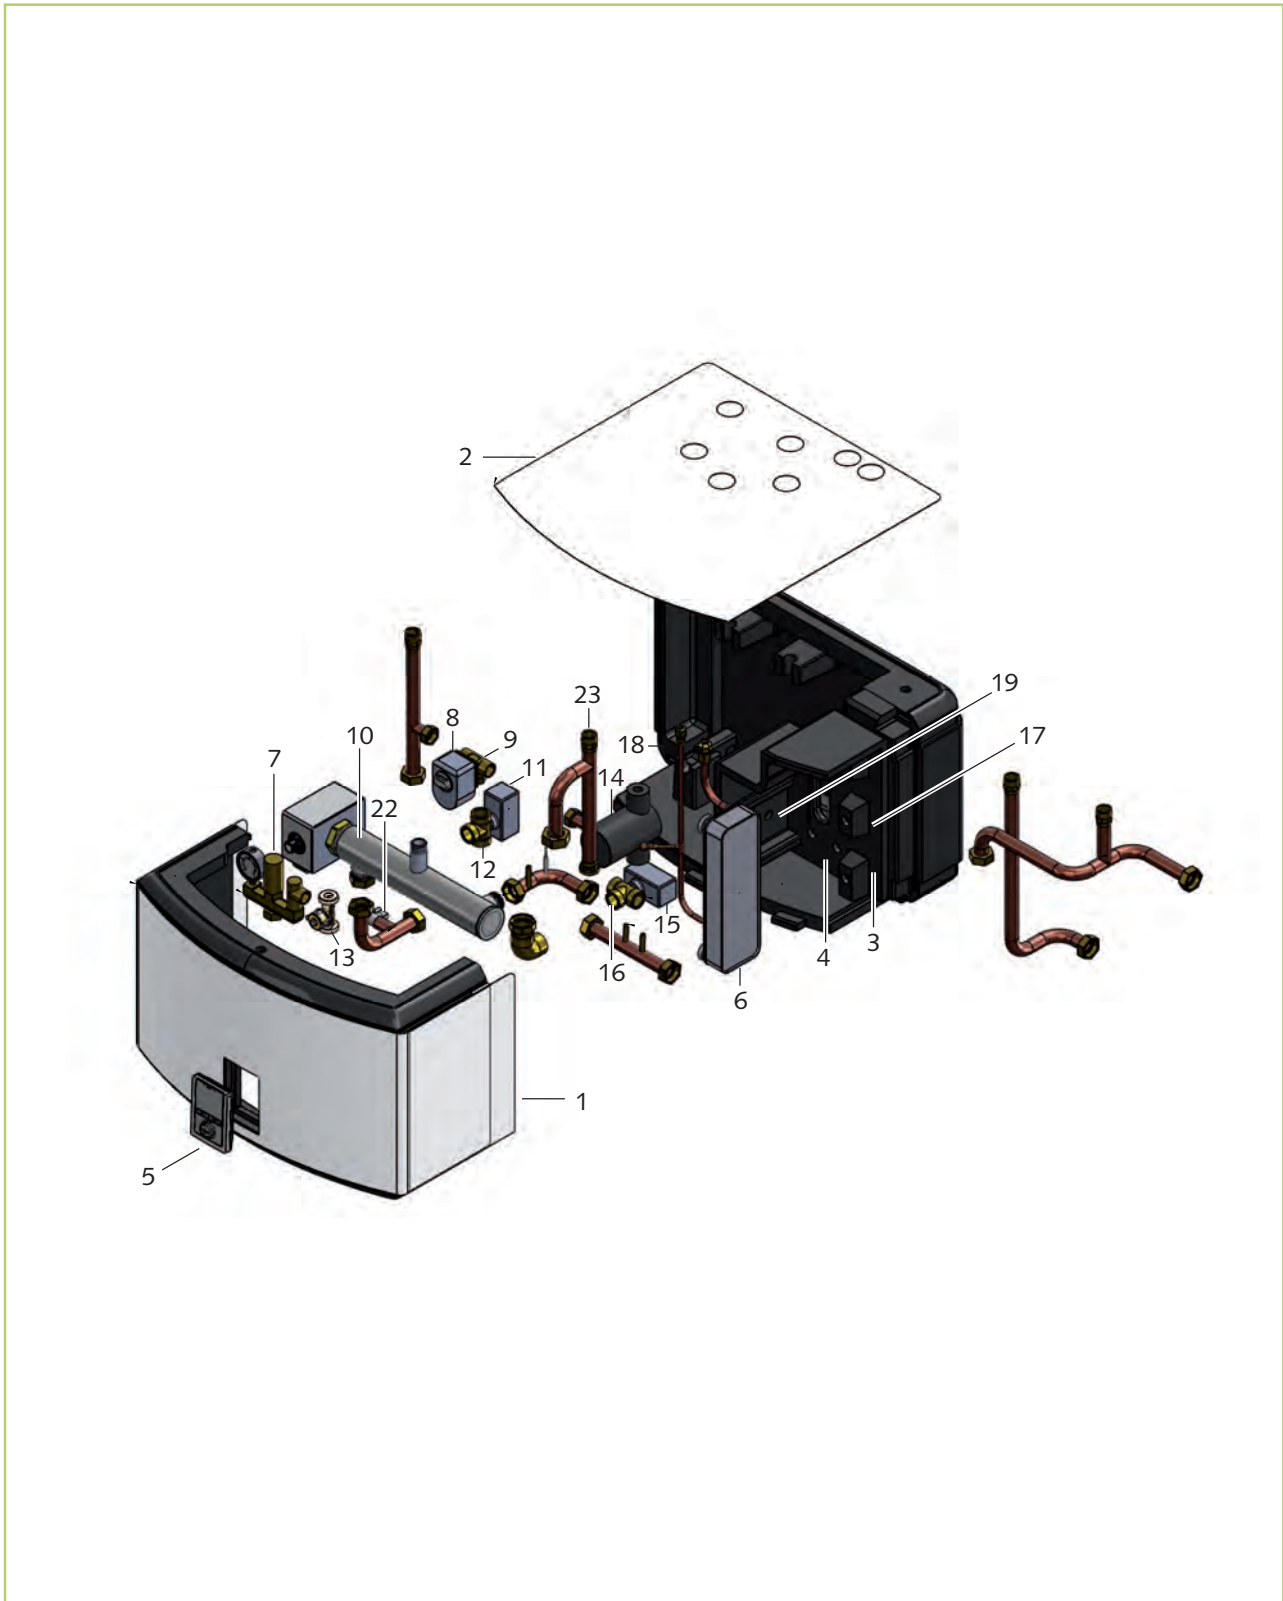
Explosionszeichnung Innenmodul WKF 85/120/180
